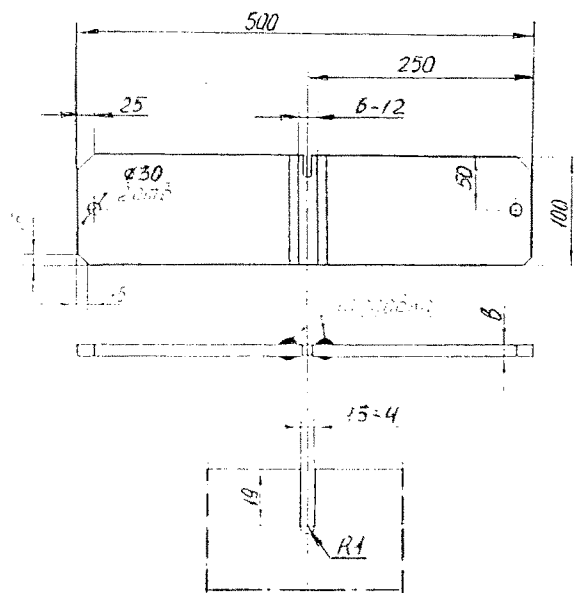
Плоский образец с наплавкой сварочных швов
